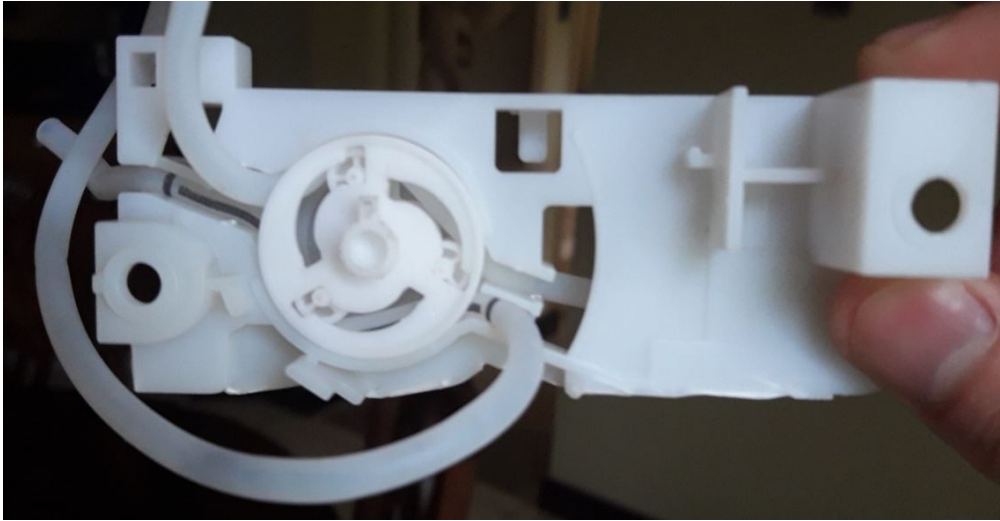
Bomba peristáltica obtenida de impresora Canon iP2700, vista frontal
